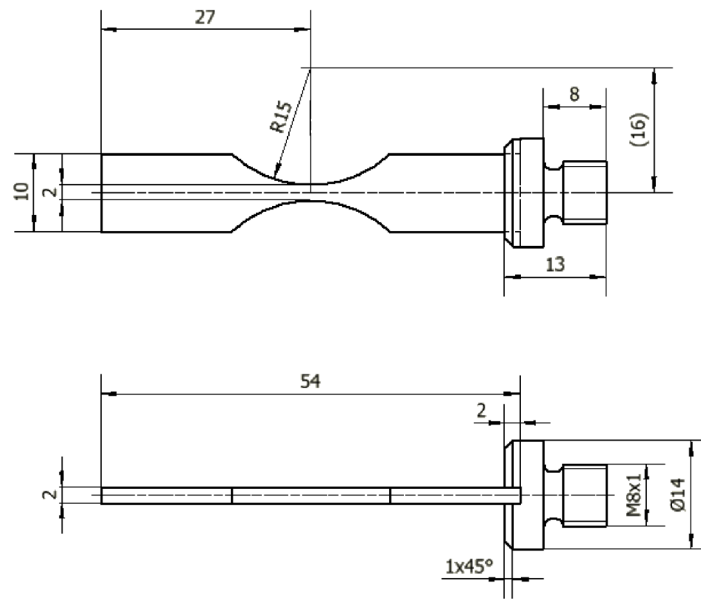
Geometrie der Flachprobe für die Ultraschallermüdung aus [4].
